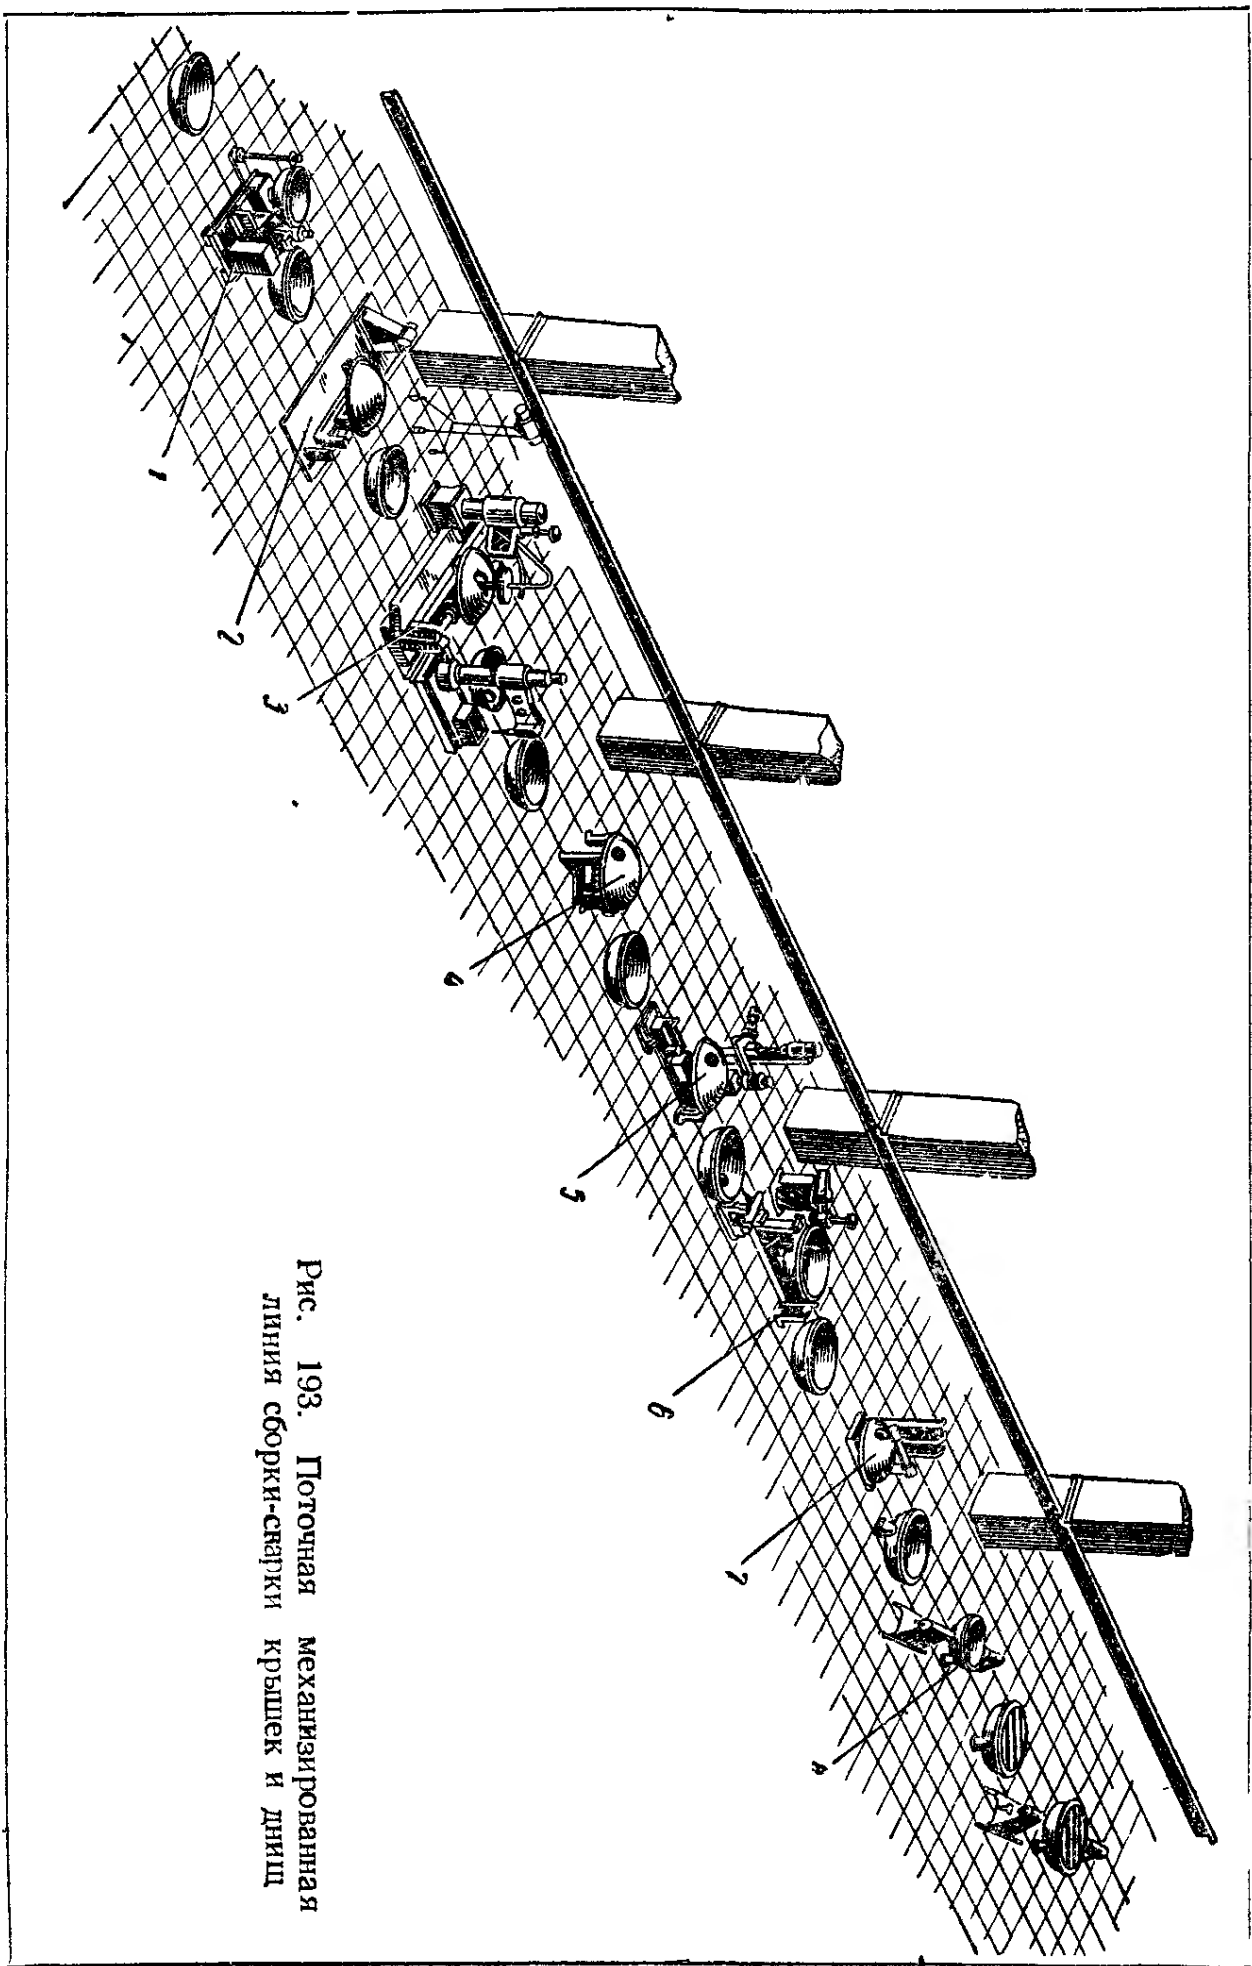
Поточная механизированная линия сборки-сварки крышек и днищ
